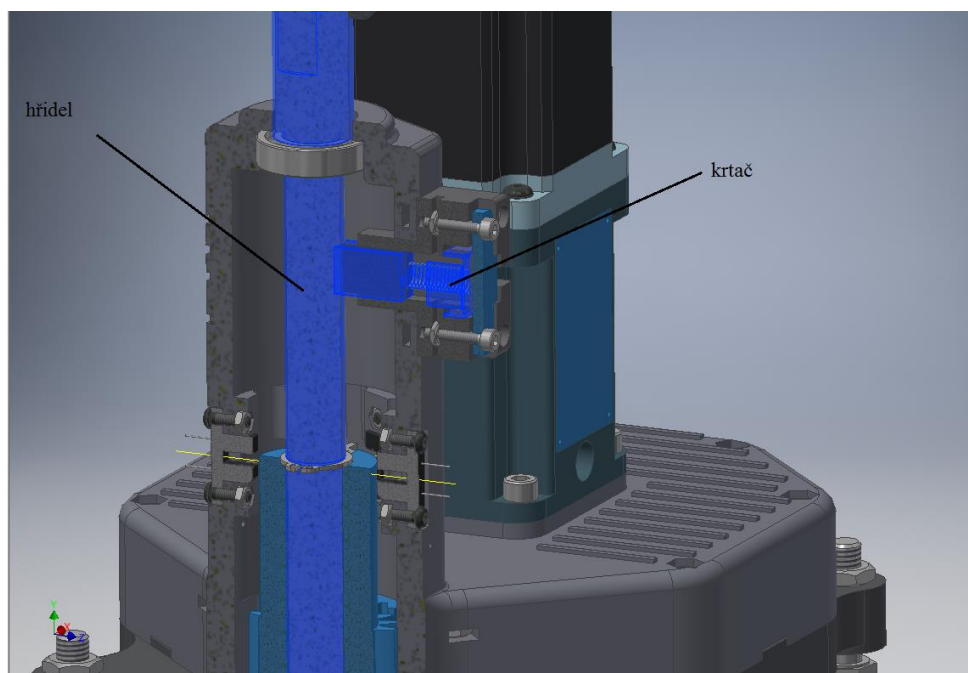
Rotující kolektor pro elektrické zvlákňování
